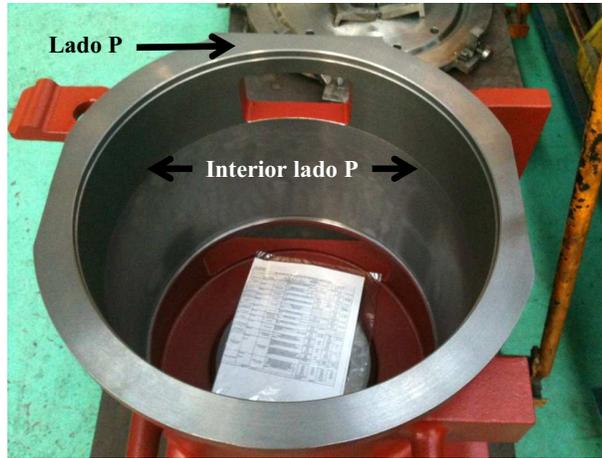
Segundo proceso de motor maquinado lado P e interior de lado P.
